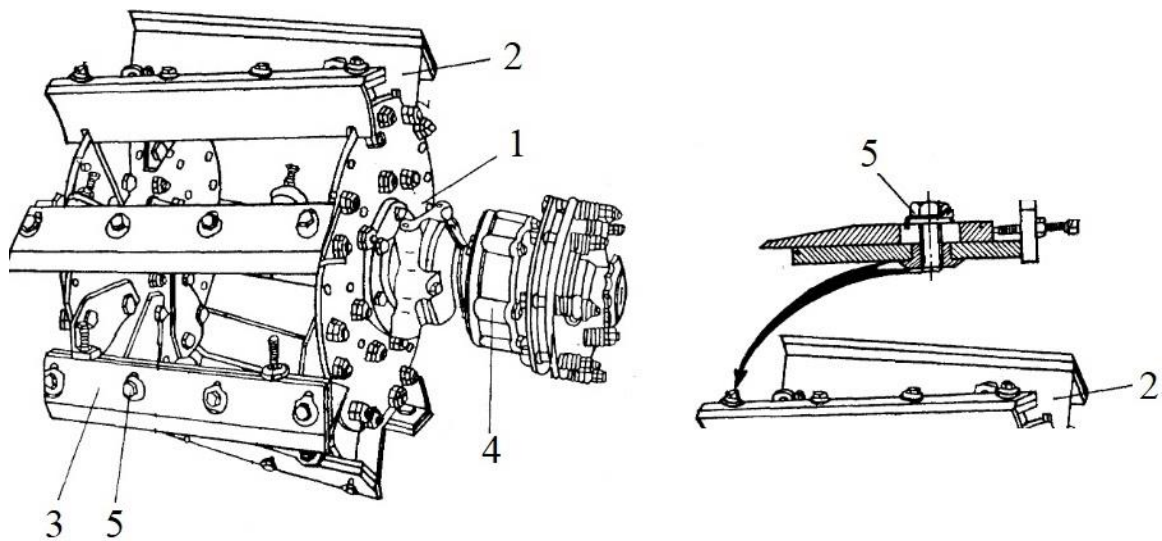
Подрібнювальний барабан: 1 – диск; 2 – лопать; 3 – ніж;
